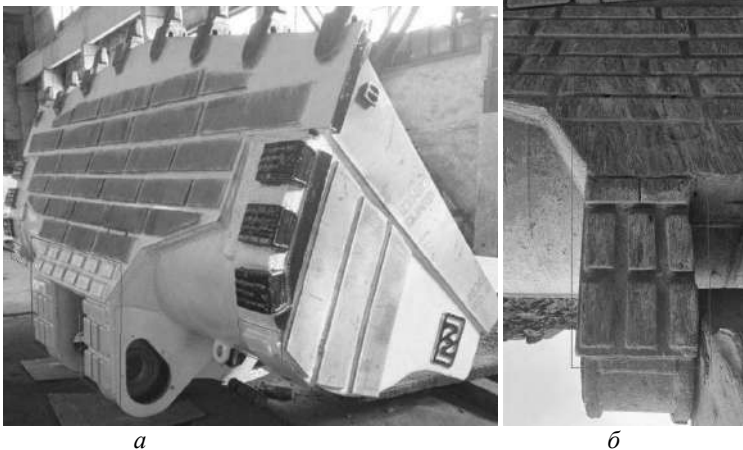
Передня частина ковша із привареними армуючими елементами (а); ліва сторона зношеної поверхні ковша (б)
